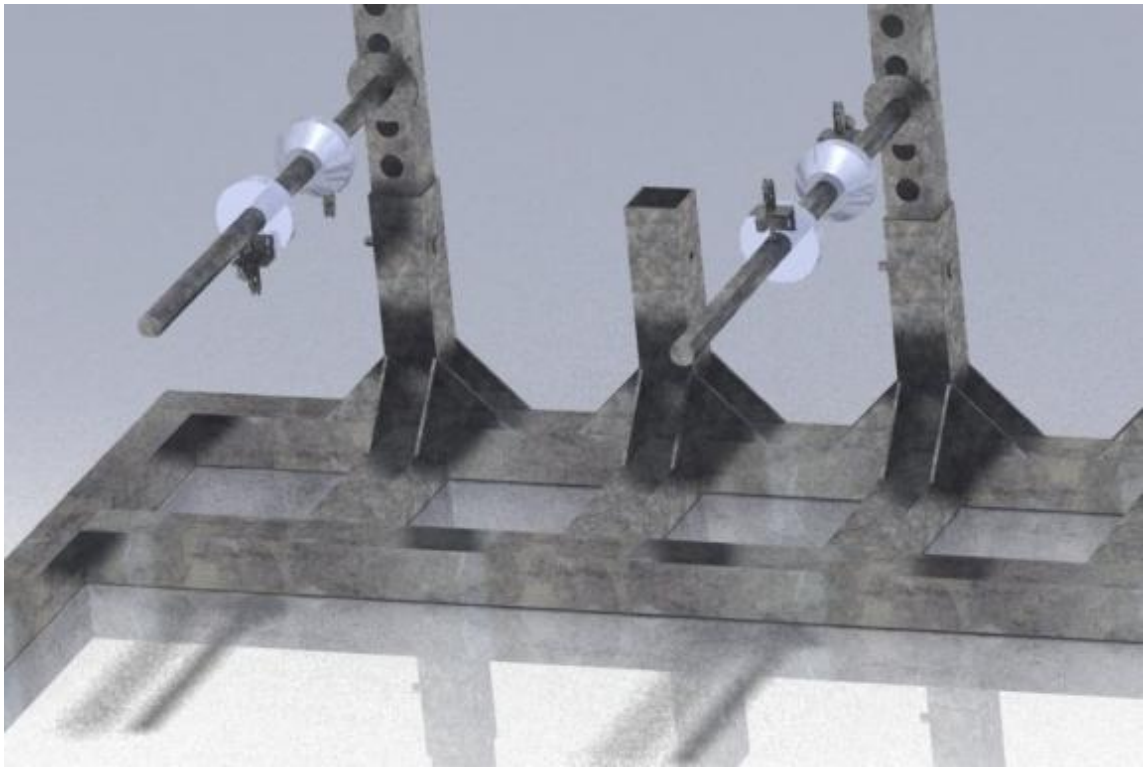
Pormenor do sistema de encaixe dos pilares verticais no estrado da estrutura
